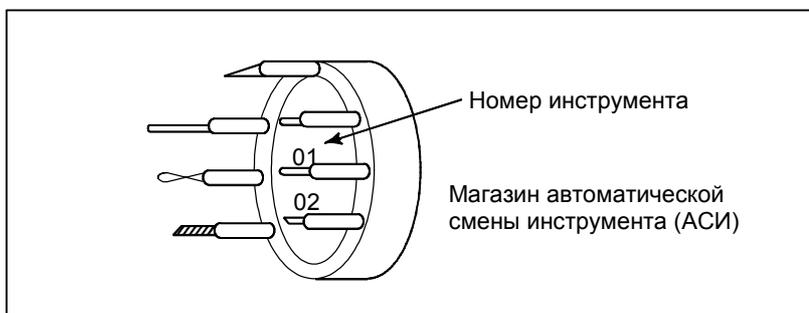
(а) Инструмент, используемый для различных видов обработки
